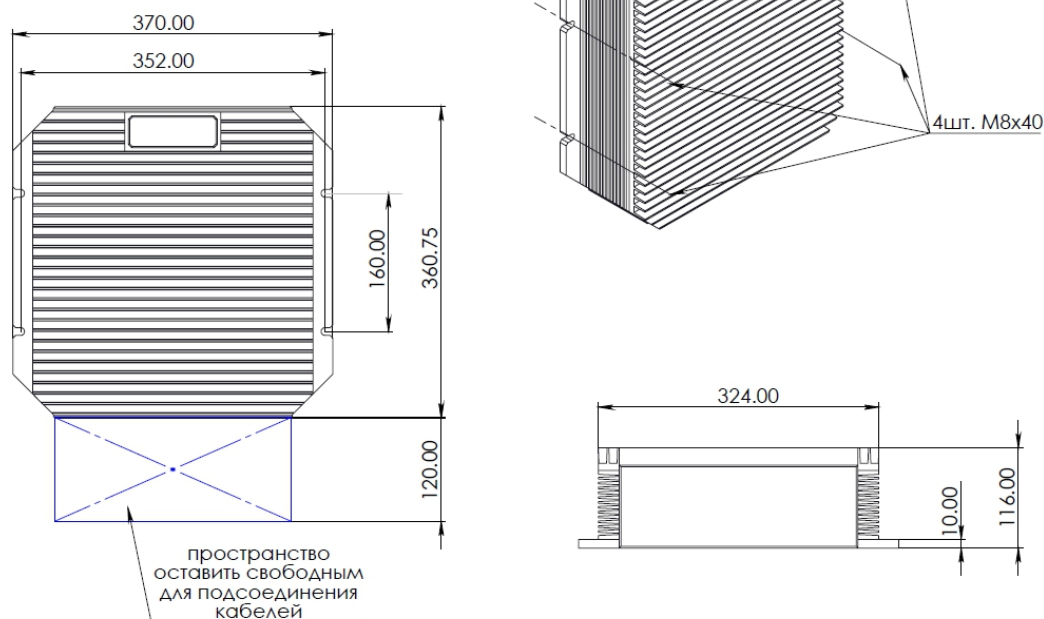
Монтажная схема и габаритные размеры корпуса медиапроцессора
